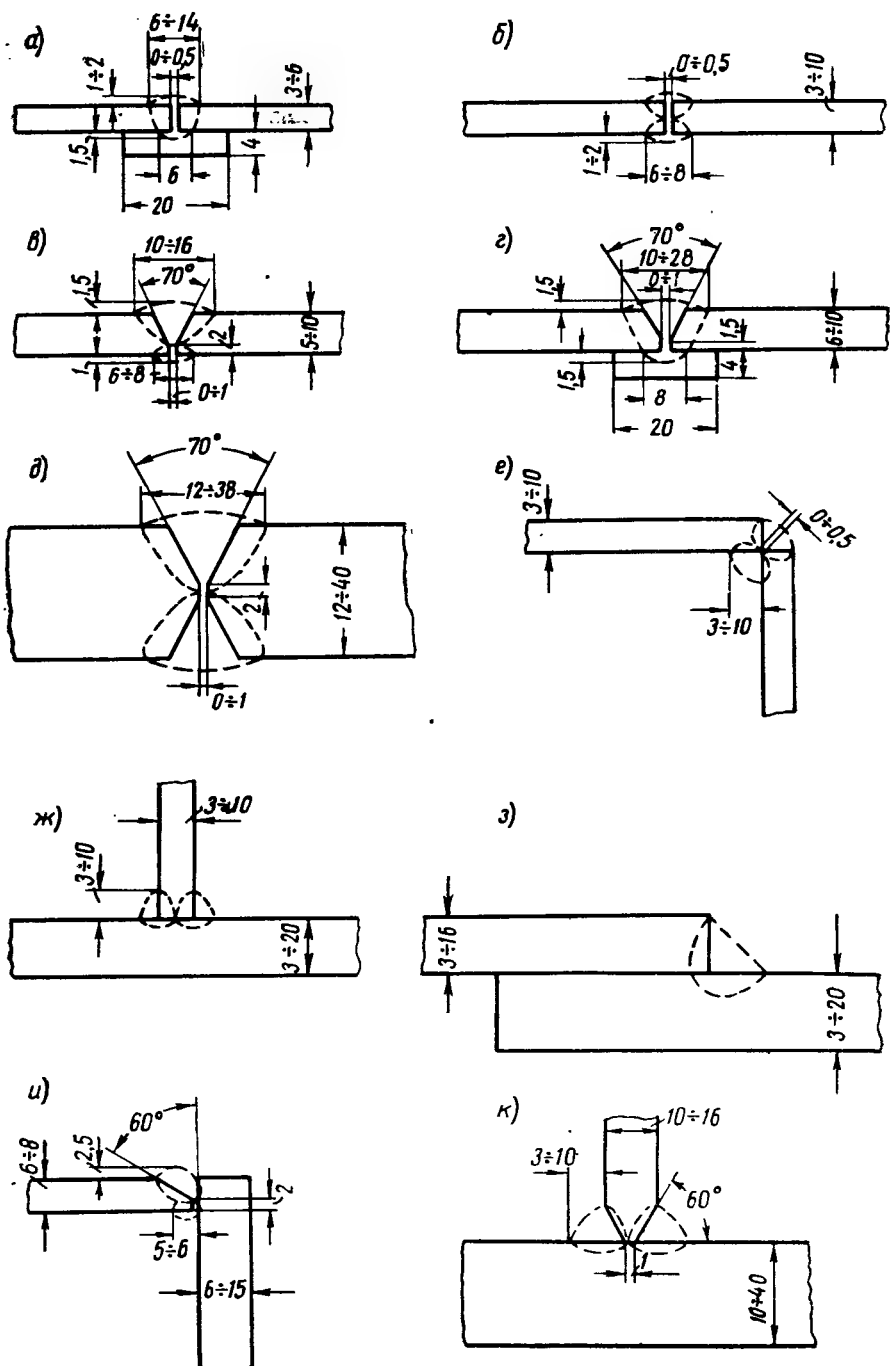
Типы и размеры сварных швов алюминиевых листовых конструкций
